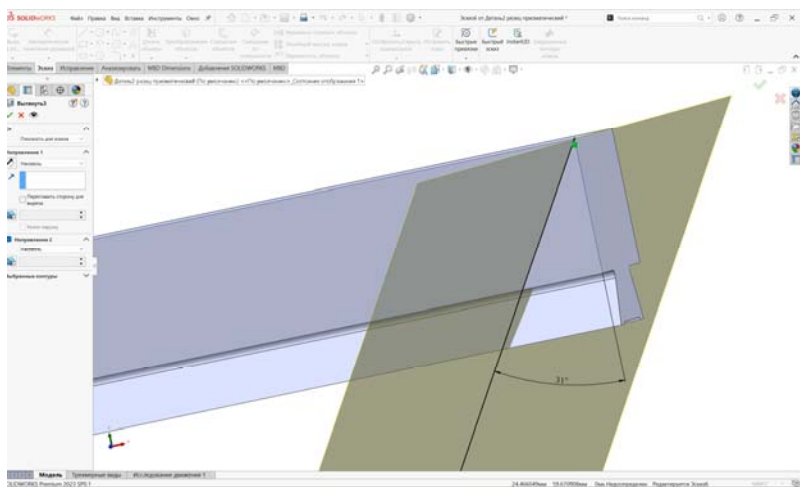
Сечение заготовки резца плоскостью под углом заточки $\varepsilon = \alpha + \gamma$
